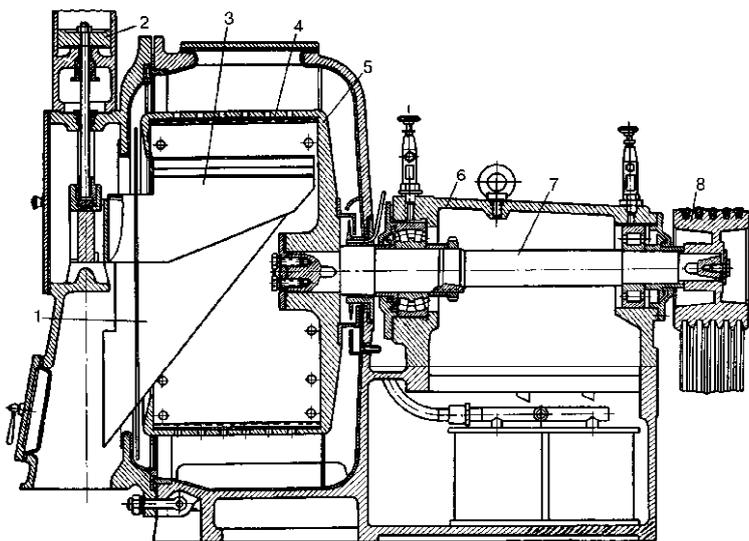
Центрифуга с ножевой выгрузкой осадка
